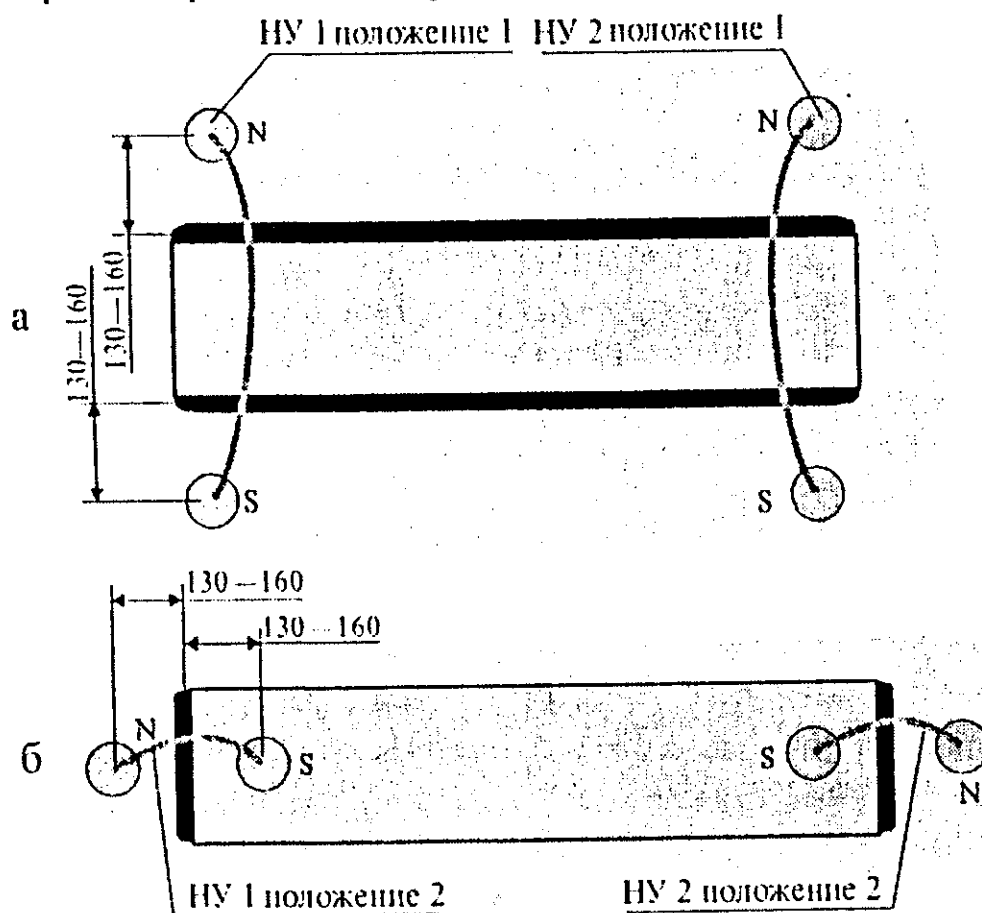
Контроль сварных швов приварки накладок с размерами одной из сторон менее 200 мм, другой — 300—600 мм
